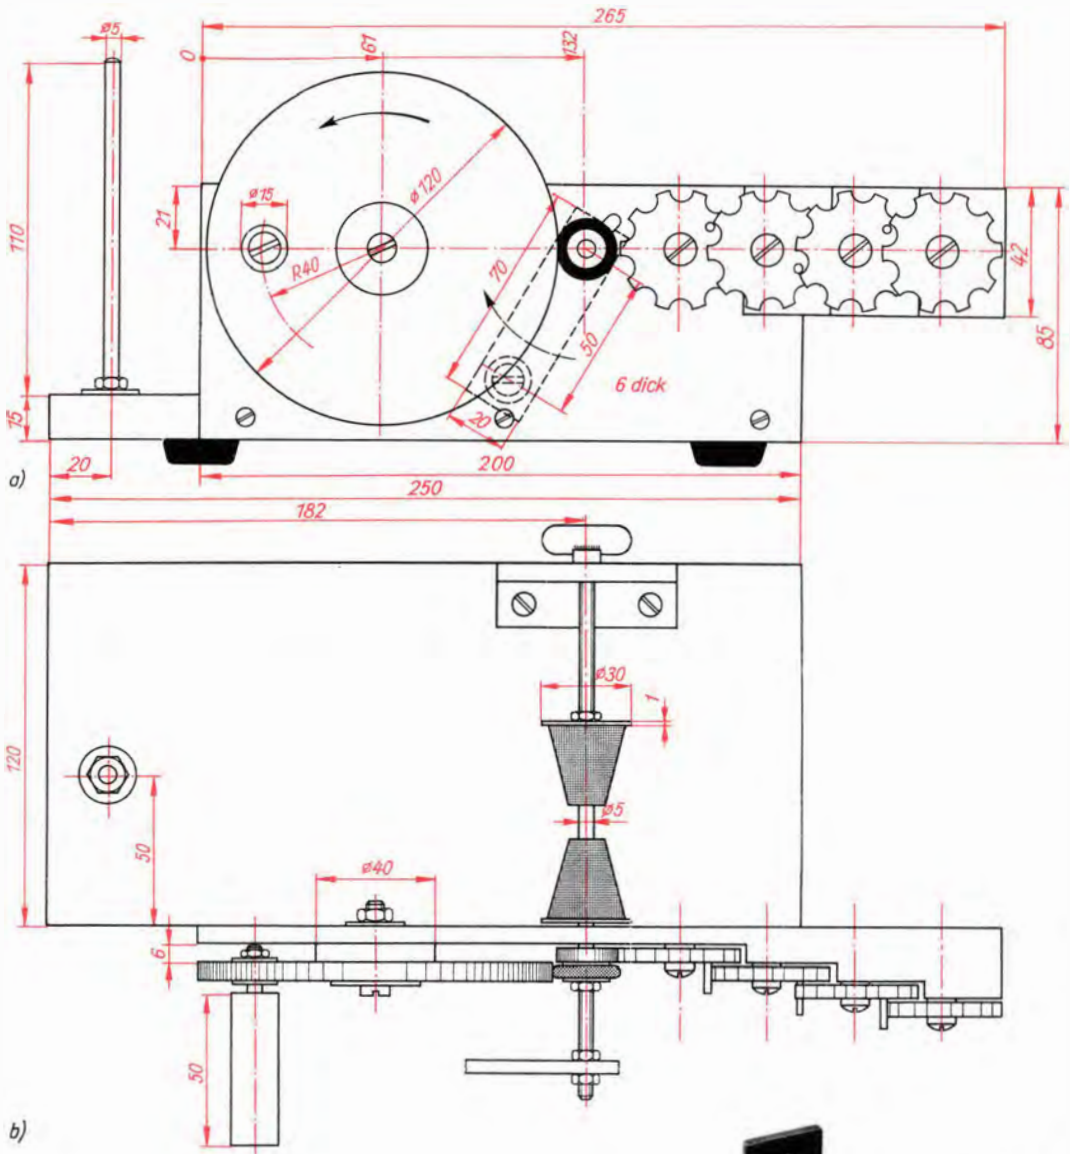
Maße der Wickelvorrichtung: a) Vorderansicht, b) Draufsicht
